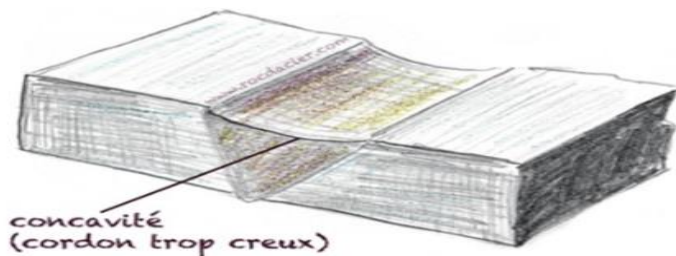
concavité dans un joint soudé (Réf.[R28])
